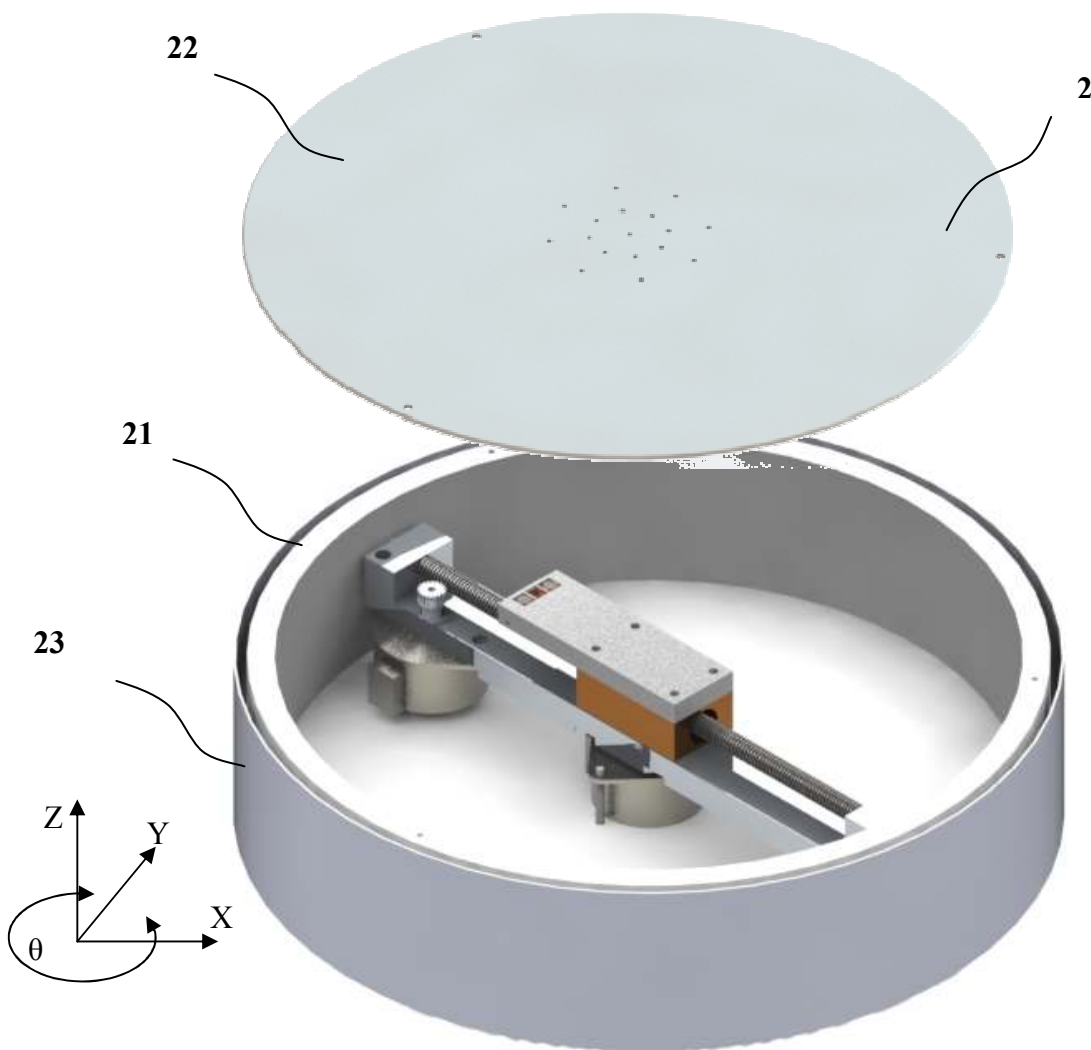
vue en 3D du porte wafer "check" de testeur sous pointes, sur le quel intégré-EDMR est adaptée et fixée.
